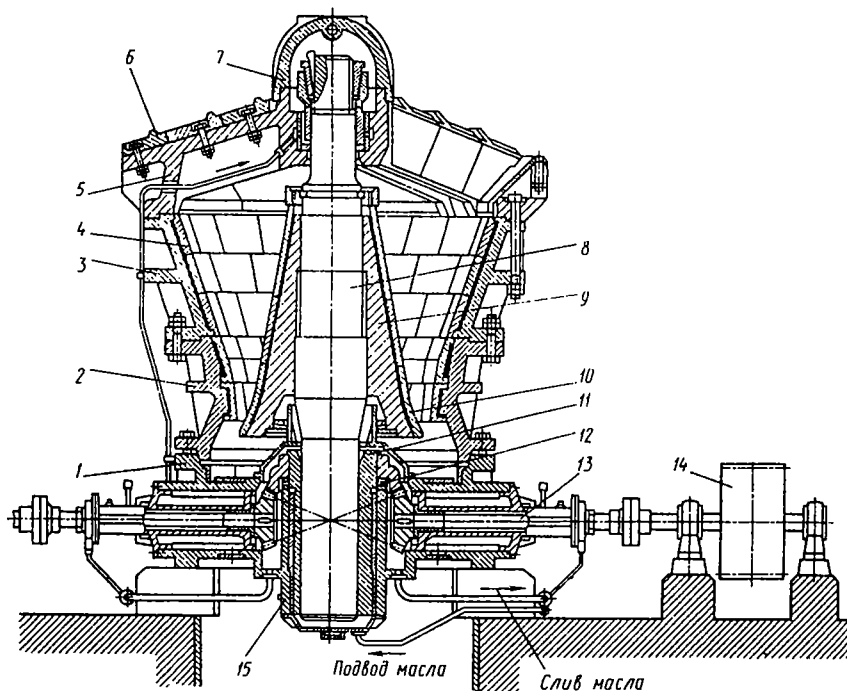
Конусная дробилка ККД-1500/180 для крупного дробления:
